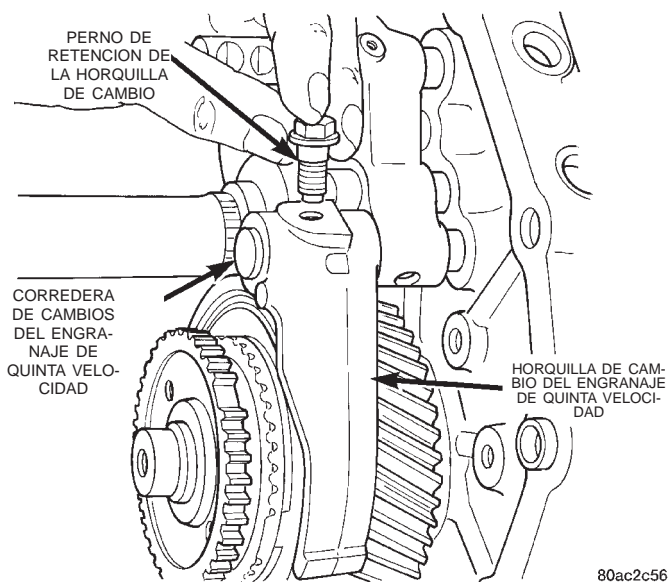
Desmontaje del perno de retención de la horquilla de cambio
